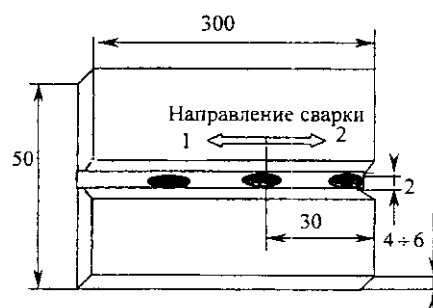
Схема прихватки и сварки медных пластин
